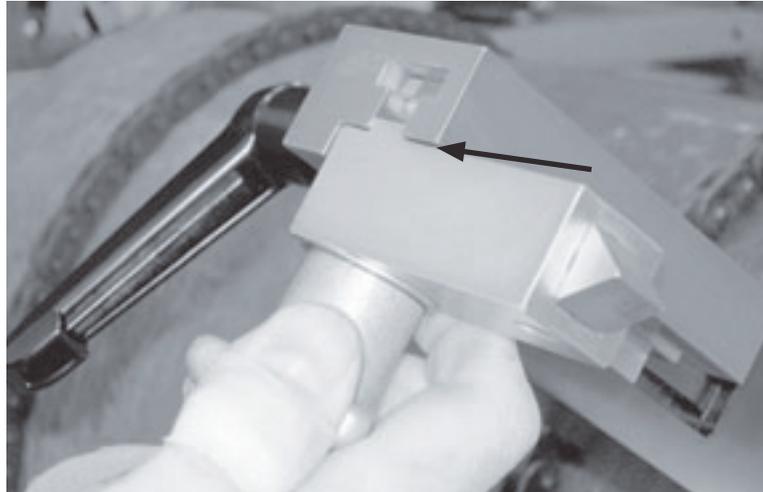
Ziehen Sie die Montagespannerschrauben gerade fest genug an, um den Werkzeugschlitten in seiner Position zu halten.
